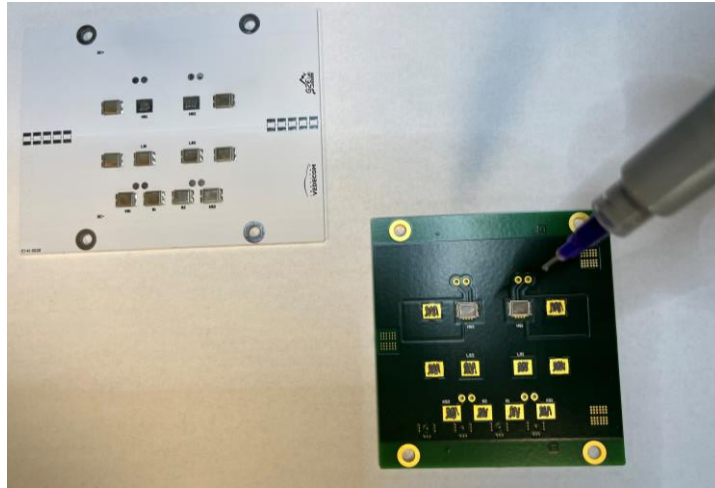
Placement de la crème à braser sur l'empreinte Drain des MOSFETs du PCB et du SMI
